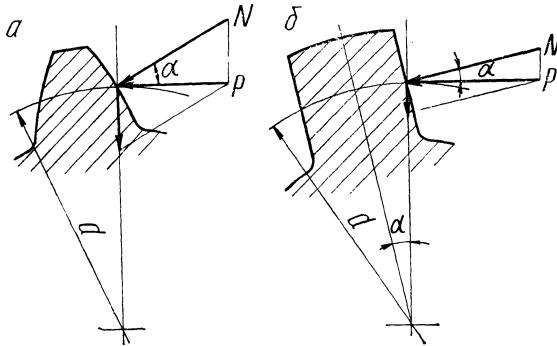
Схема действия сил на боковой поверхности шлицев для эвольвентного (а) и прямобоочного профиля (б).
